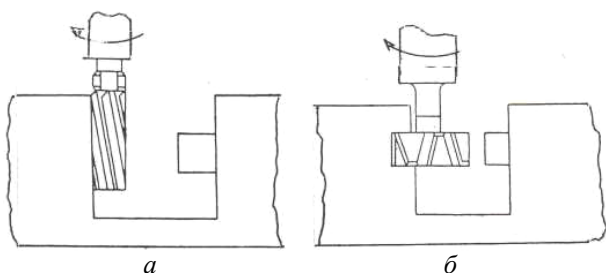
Схема фрезерования корпуса патрона: а – изломанного выступа корпуса; б – паза корпуса
